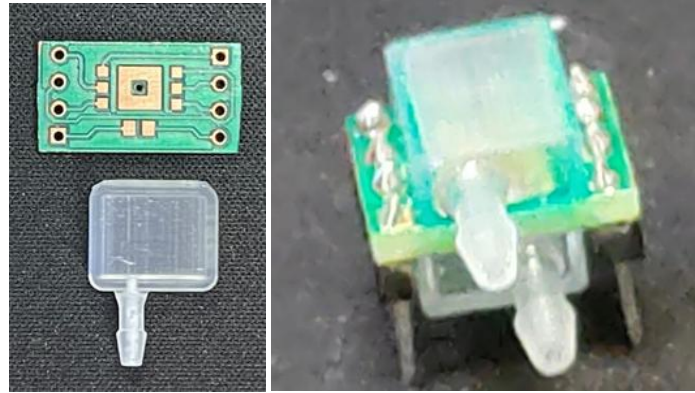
Chips y carcasa para empaquetado de chips y chip ya empaquetado listo para pruebas electromecánicas.
